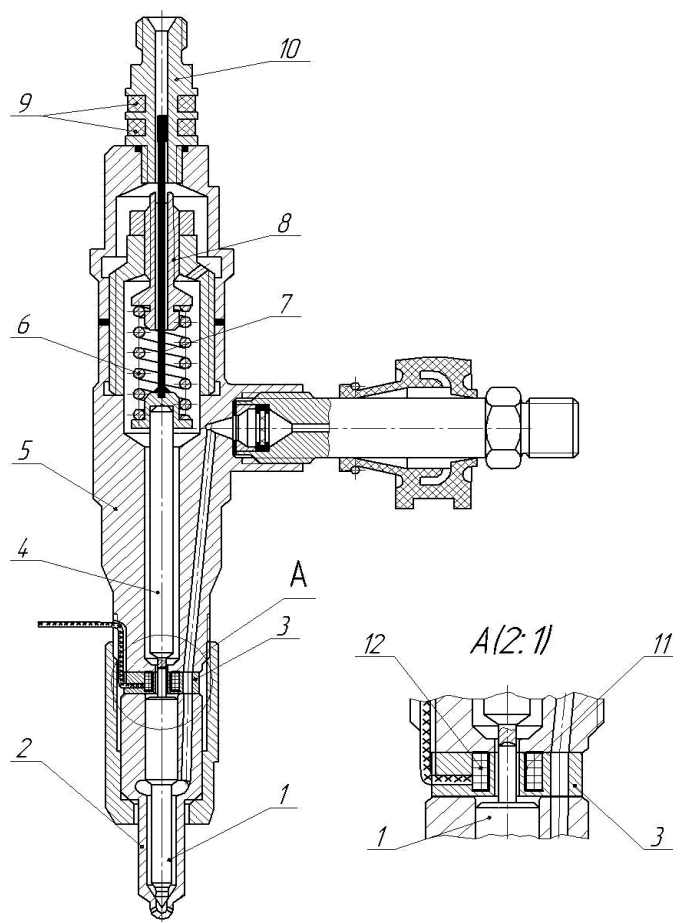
Форсунка с индуктивными датчиками перемещения иглы: 1 – игла распылителя; 2 – корпус распылителя; 3 – датчик – «проставка»; 4 – штанга; 5 – корпус форсунки; 6 – пружина; 7 – шток; 8 – винт; 9 – катушки; 10 – датчик индуктивный; 11 – «проставка» с катушкой 12
